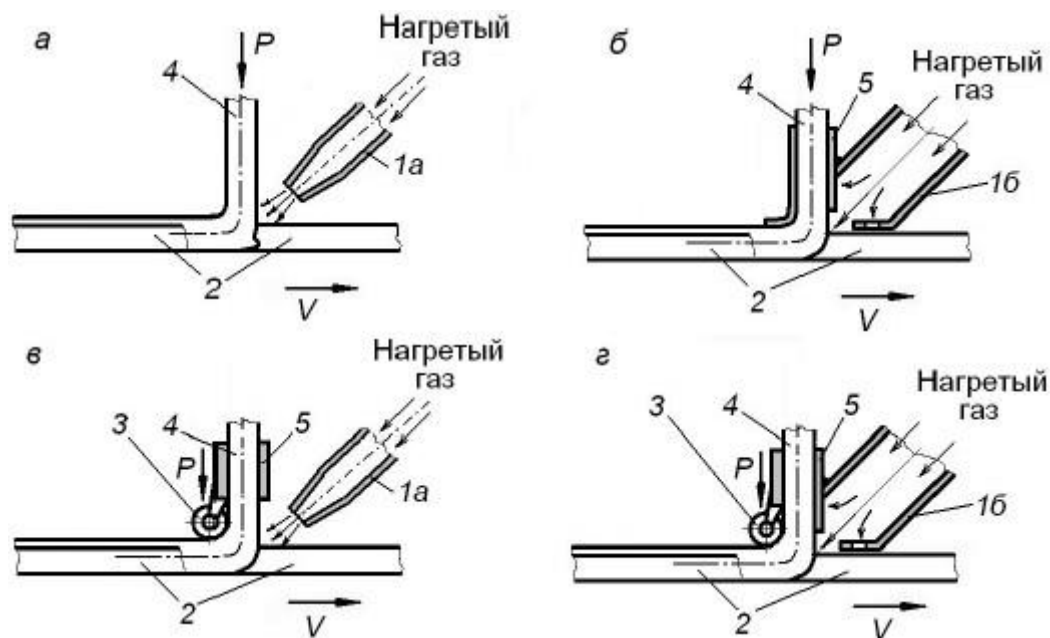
Схемы сварки с присадочным прутом: а – ручная сварка горелкой со стандартным соплом для твердых термопластов; б - ручная сварка горелкой с производительным соплом для твердых термопластов; в – ручная сварка стандартным соплом для мягких термопластов; г – механизированная сварка твердых и мягких термопластов; 1а – стандартное сопло; 1б – производительное сопло; 2 – основной материал; 3 – прижимной ролик; 4 - присадочный пруток; 5 – направляющий канал; P – направление давления на присадочный материал; V – направление сварки
